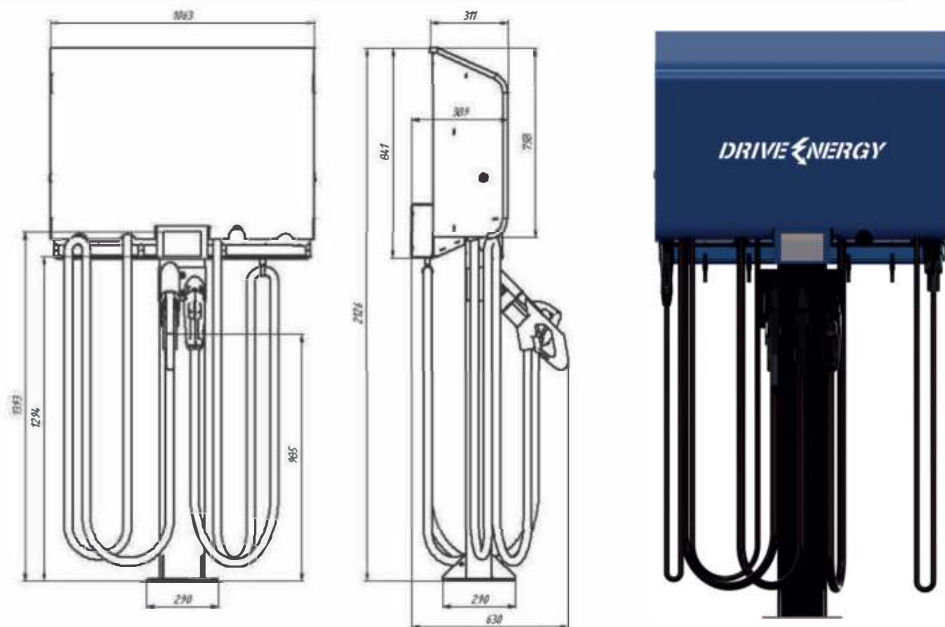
Внешний вид и размеры станции при напольном монтаже
